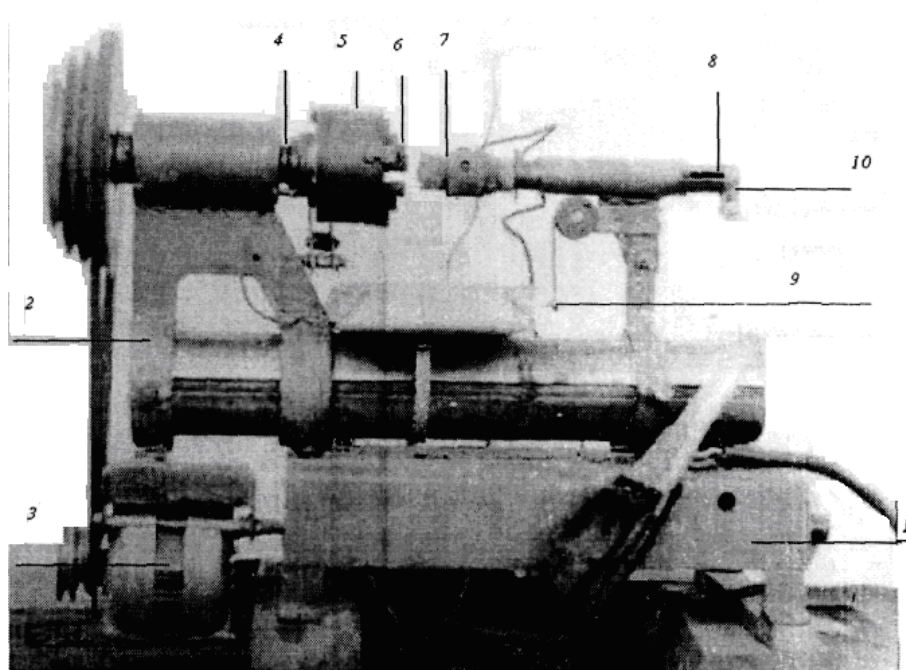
Установка для нанесения покрытий на образцы натиранием на базе токарного станка.
